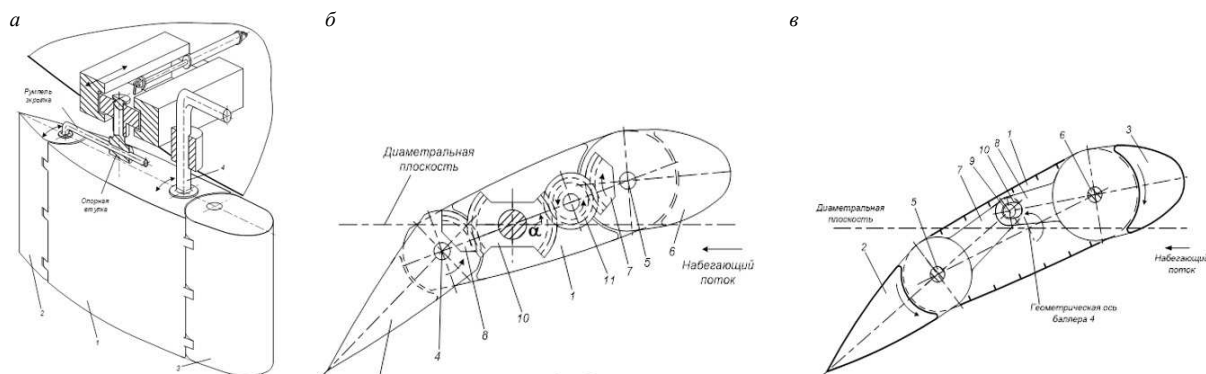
Руль с предкрылком и закрылком: общий вид (а) [3]; зубчатый (б) [4] и рычажный (в) [5] приводы синхронного поворота предкрылка и закрылка
